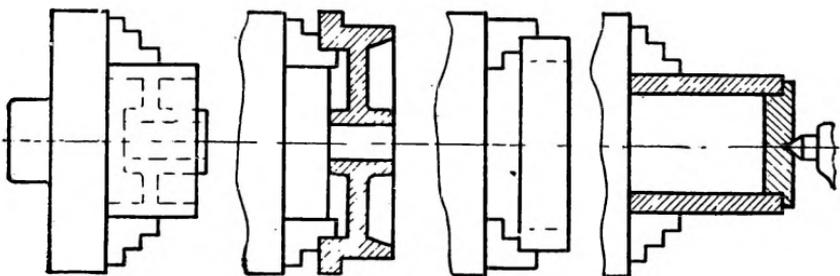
Способы крепления заготовок в кулачковом патроне.
